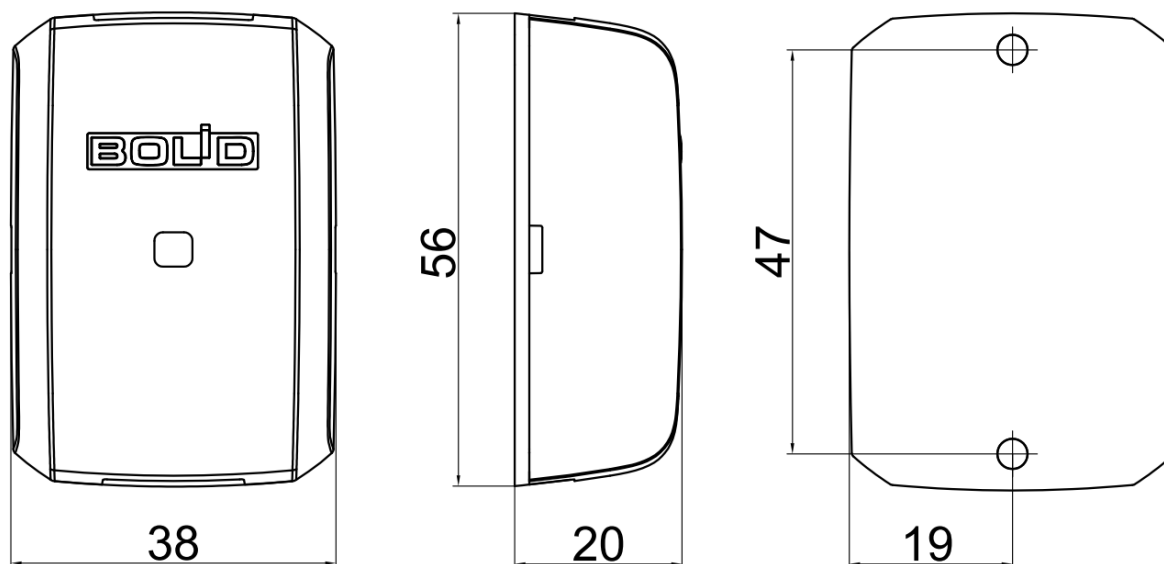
Внешний вид, габаритные и установочные размеры модуля.
